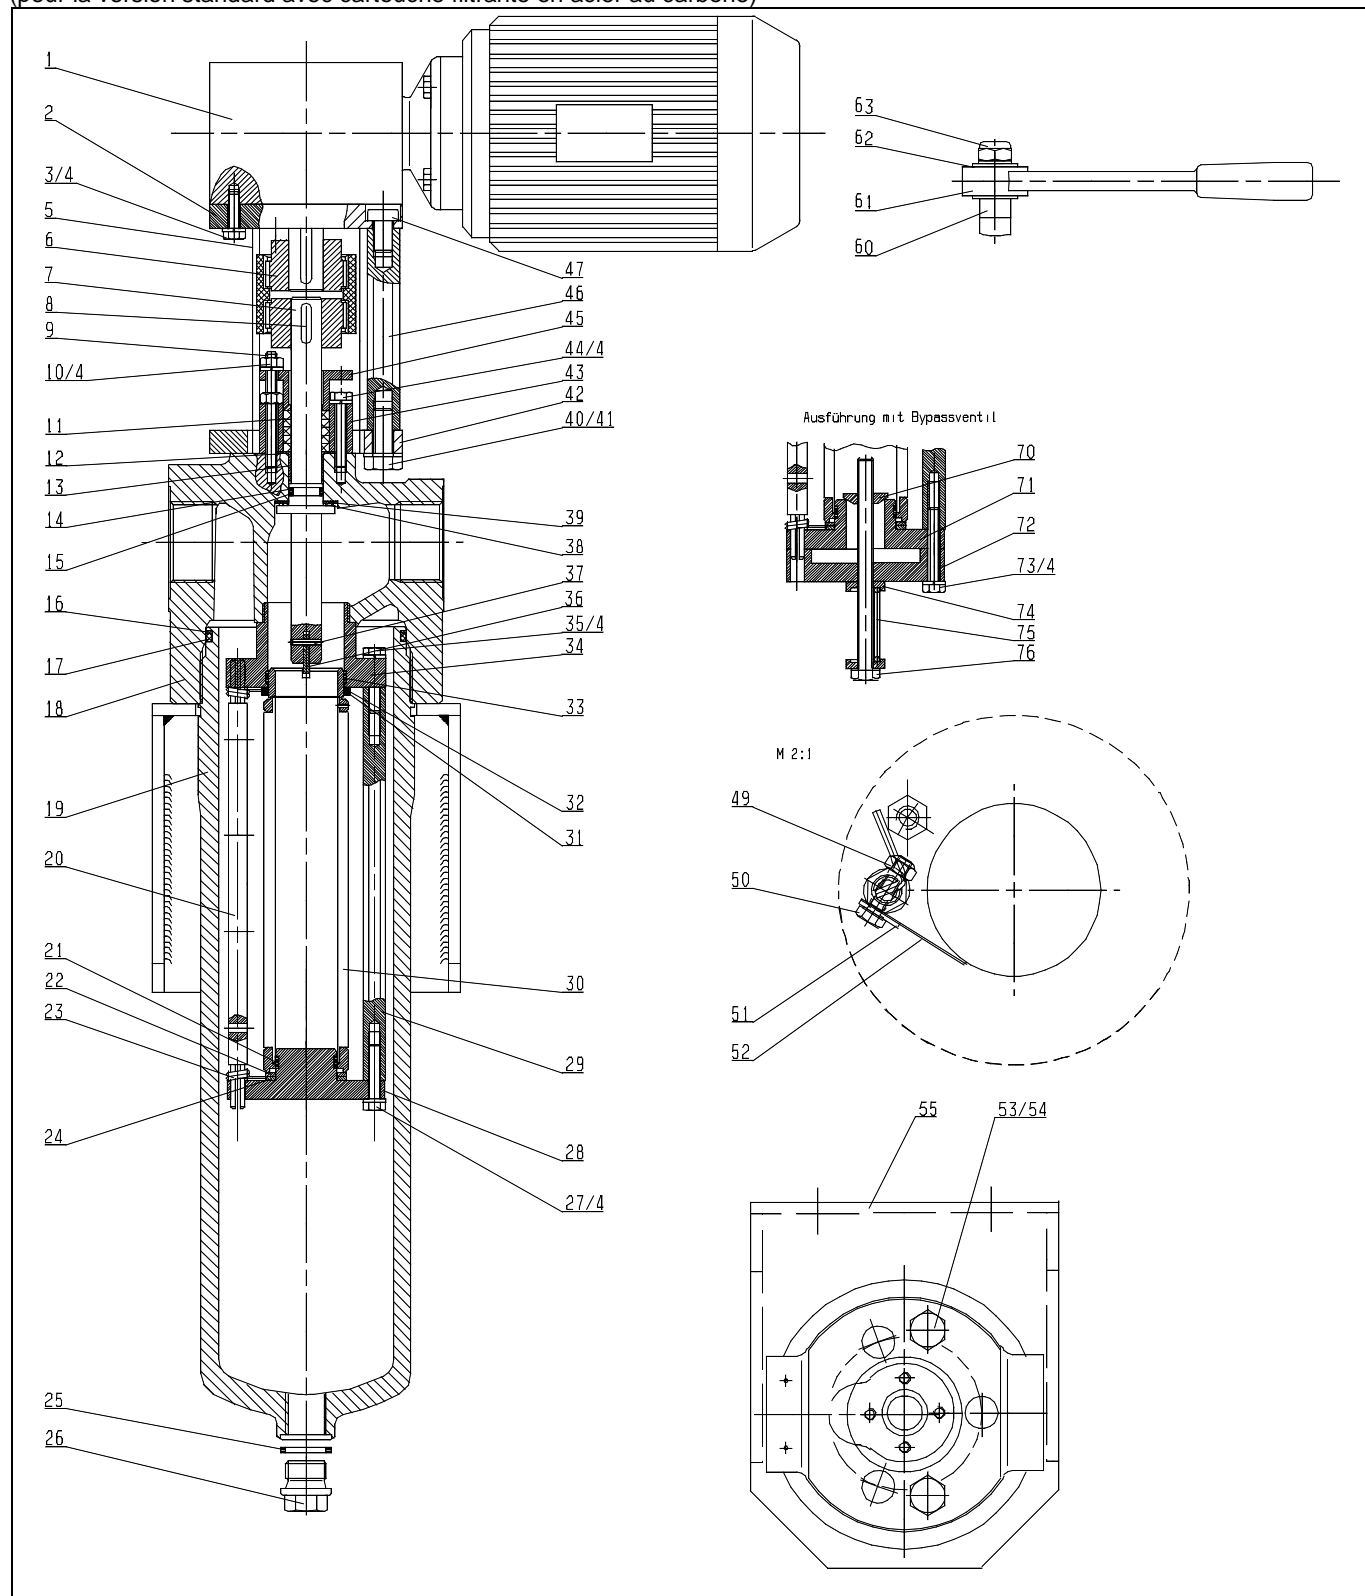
Dessin de pièces de rechange AF 71H (n° ident. 971.925.3)
